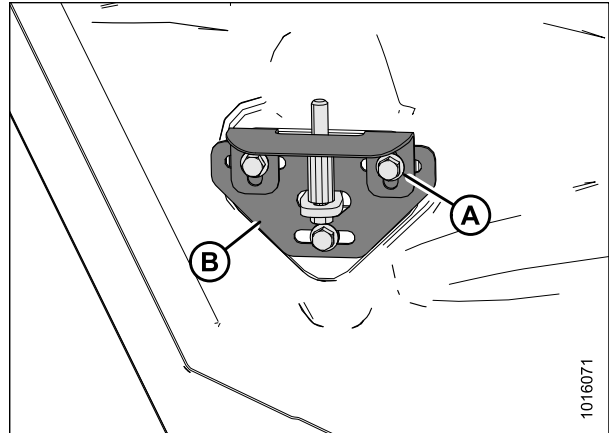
Ensamble el conjunto del pestillo de la tapa lateral izquierda
